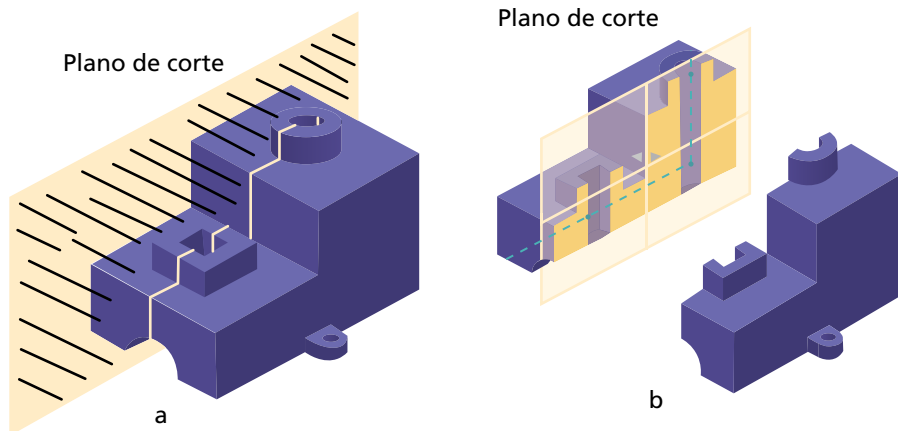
Cortes: a) plano de corte; b) plano de corte e interior de la pieza
